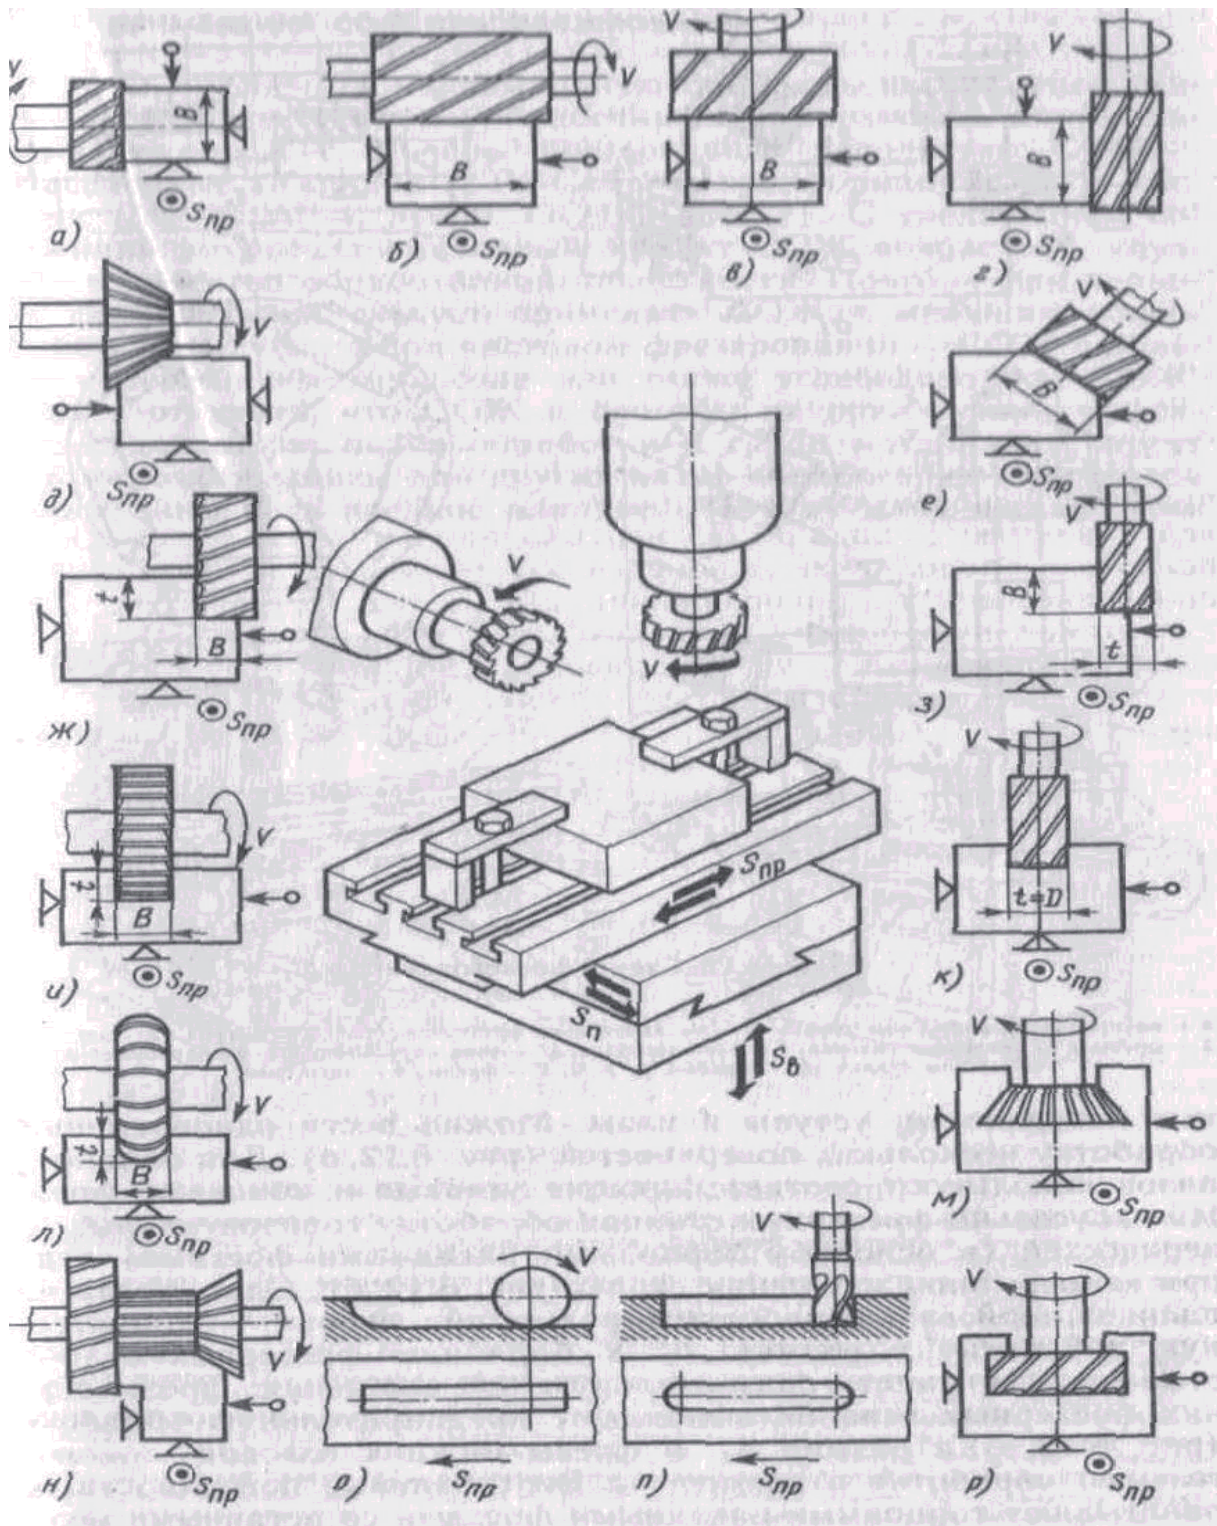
Обработка поверхностей заготовок фрезерованием
